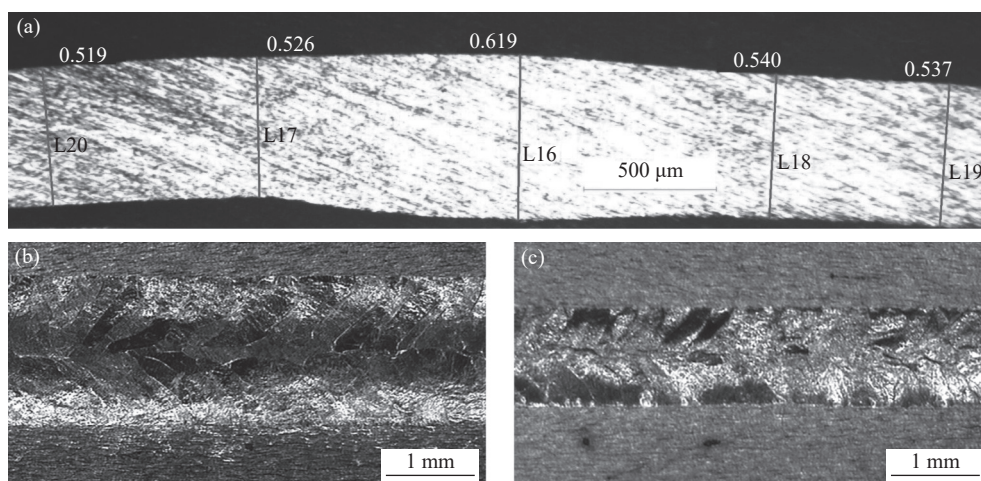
为大口径薄壁钛焊管焊缝形貌,表 4 为焊缝宏观尺寸。可以看出 Gr.1 纯钛薄壁焊管焊接接头均实现双面良好成型,焊缝正面和背面连续均匀。由于激光焊接过程中激光束具有更强的穿透性且激光能量更加集中,致使激光焊接接头外焊缝宽度仅为 1.5 mm,内焊缝宽度为 0.98 mm,相比于传统 TIG 焊接,激光焊接接头焊缝区和热影响区宽度均明显较窄。
